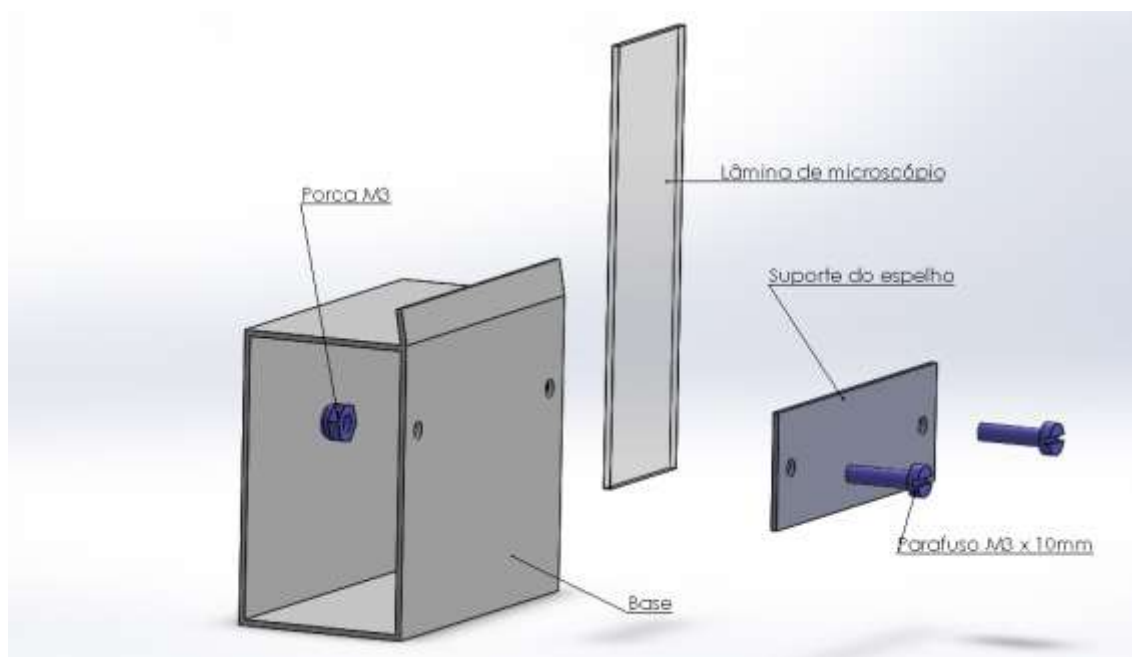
Suporte de lâmina de microscópio. Vista explodida.
